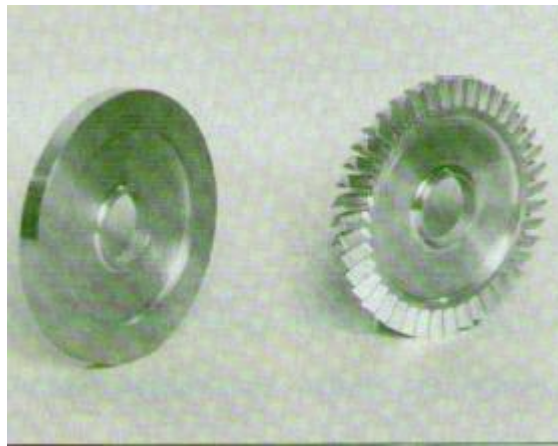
Заготовка для обработки статора и изготовленная с применением HSC деталь
